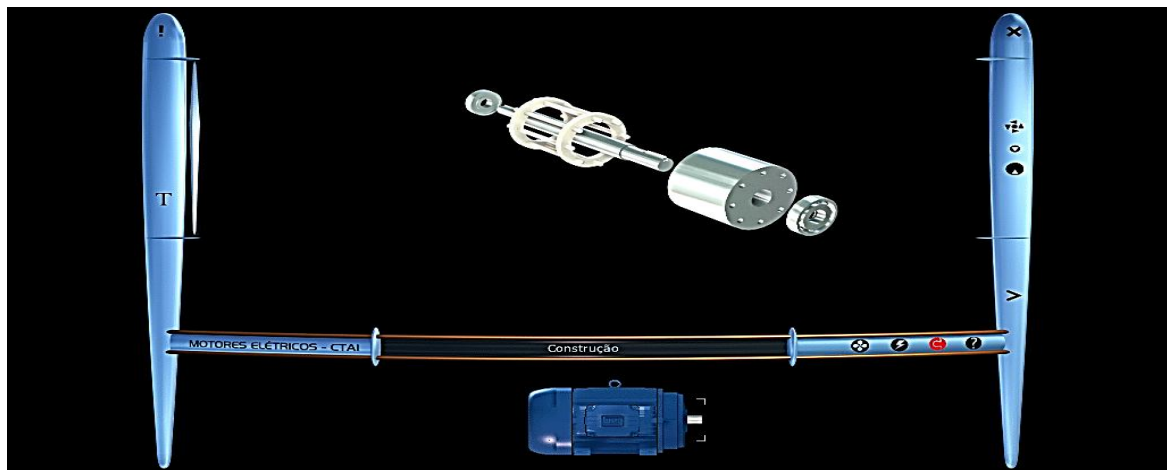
Partes de un motor trifásico (armadura).
